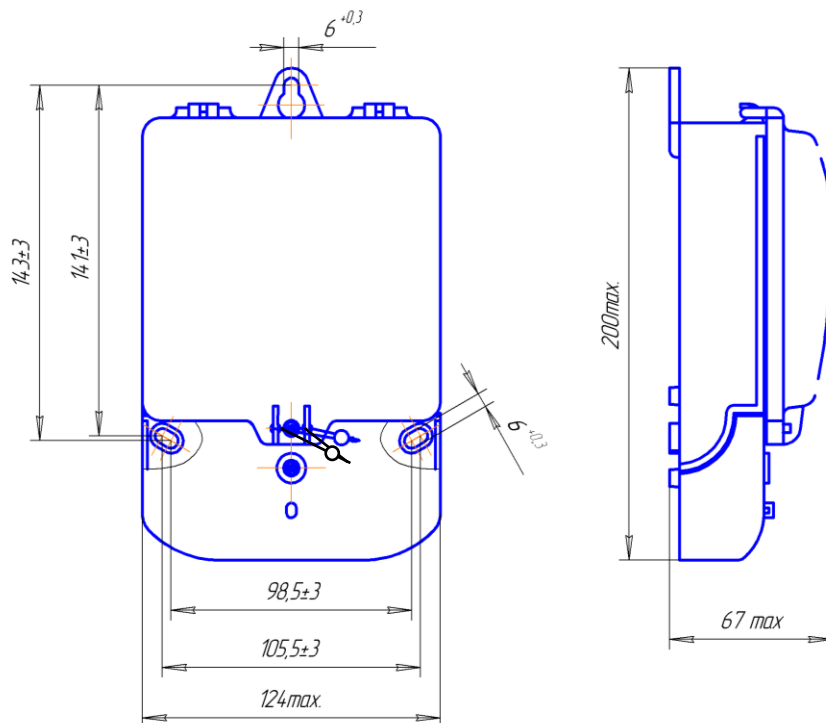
Габаритный чертеж и установочные размеры счетчика (для счетчиков с типом корпуса Н1)
